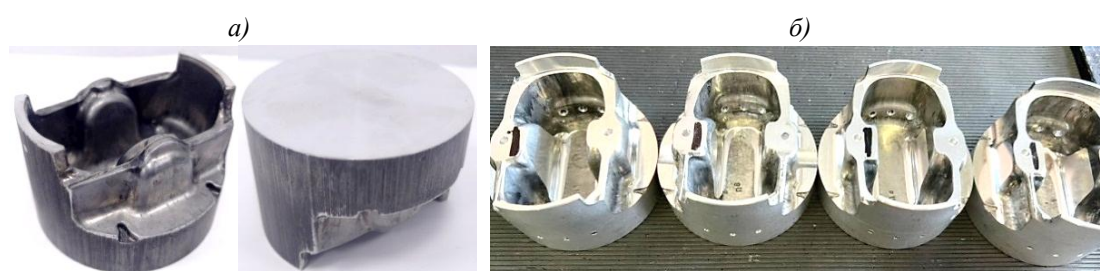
Заготовки поршней из металлического композиционного материала на основе алюминиевого сплава системы Al–Cu–Mg–Si, армированного тугоплавкими частицами SiC, после штамповки (а) и перед чистовой обработкой (б)
